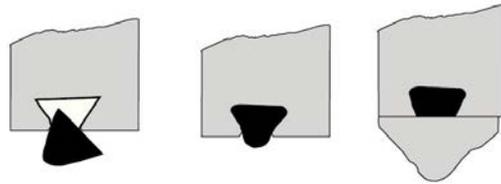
Joint trapézoïdal axial (joint de la chambre)
